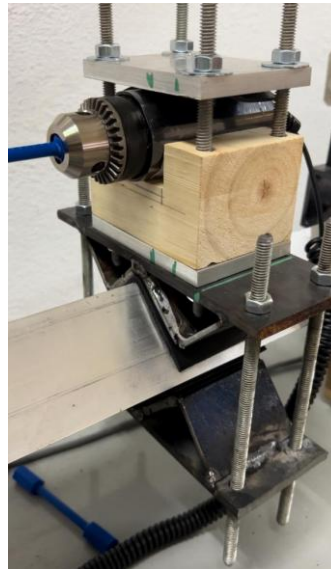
Utillaje para adaptación de torquímetro en máquina de torsión.
